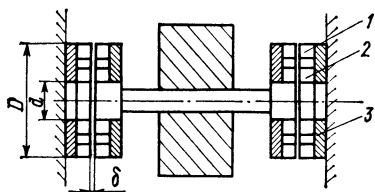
Радиальный высокоскоростной магнитный подшипник
